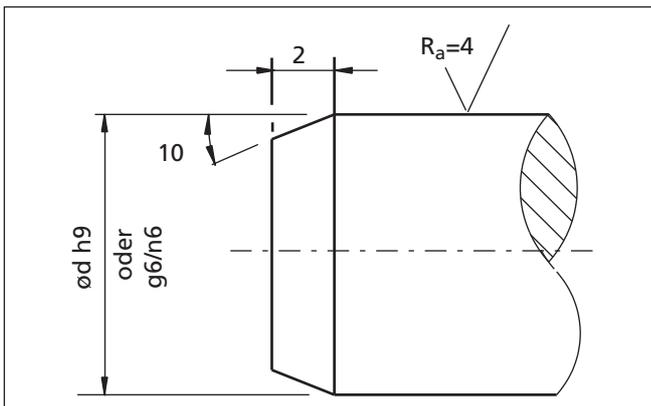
Durchmesser tolerance, Oberflächenrauheit und Kantenfäse der Welle
